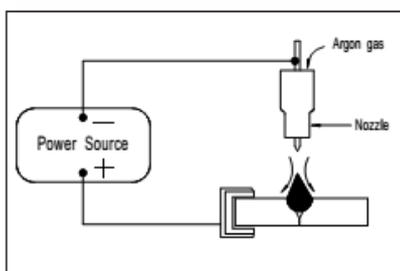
Дуга при сварке в режиме TIG
